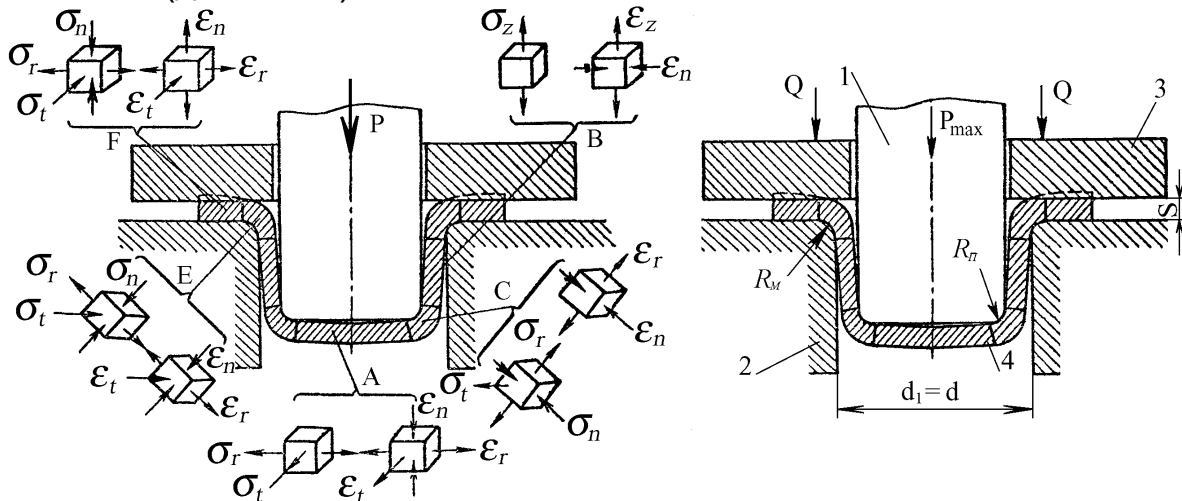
Схема напружено-деформованого стану і зусилля, що діють в окремих ділянках у процесі витягування (1 – пуансон; 2 – матриця; 3 – притискач; 4 – заготовка)
